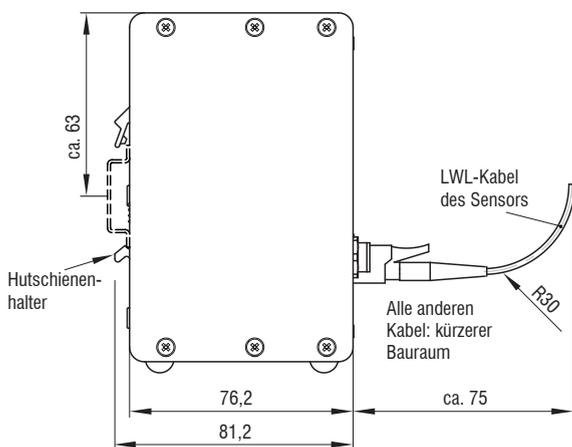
Maßzeichnung Frontansicht des IMC5420 Controllers, Abmessungen in mm (Zoll)
